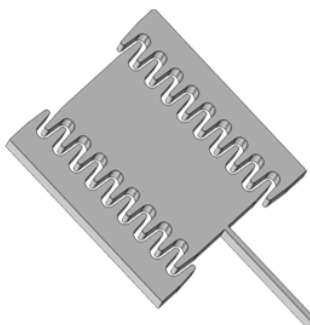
Гребенки резонатора с трапецевидными скругленными пальцами
